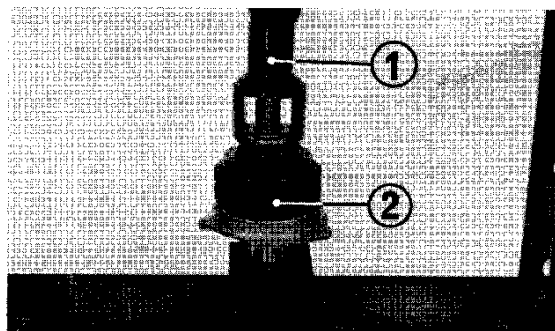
(1) Dämpfungsfeder-Ausbauwerkzeug
